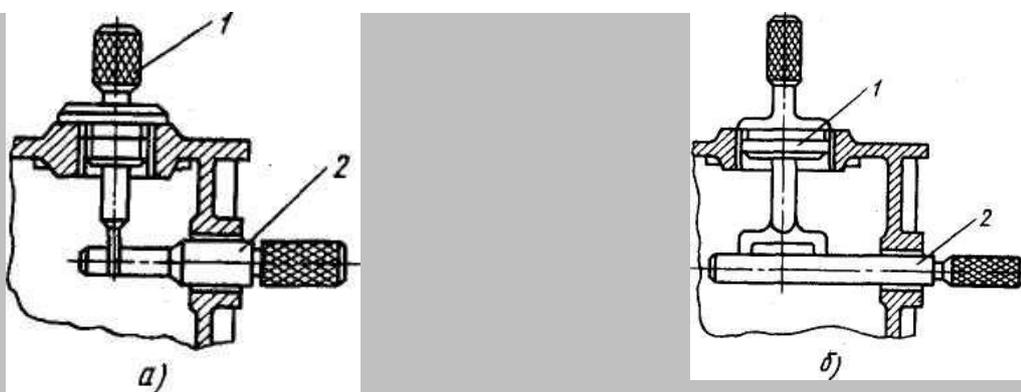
Способы контроля расположения осей отверстий в корпусе редуктора конической зубчатой передачи: а — калибром с отверстием, б — калибром с лапкой; 1, 2 — калибры
